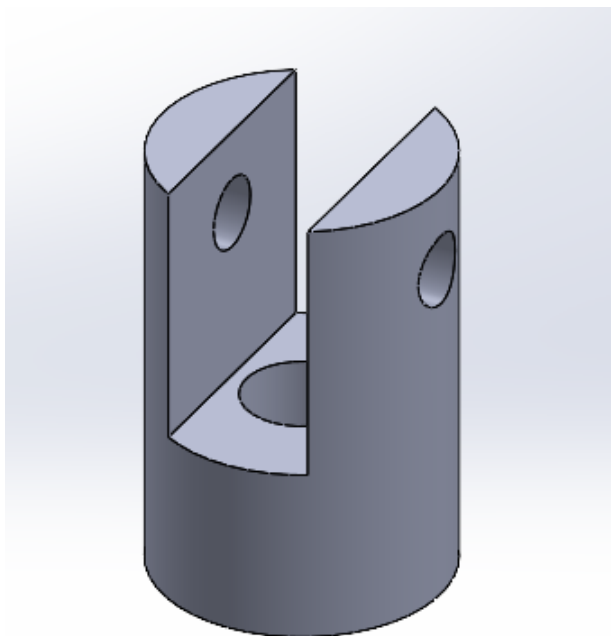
Деталь для штока пневмоциліндра
